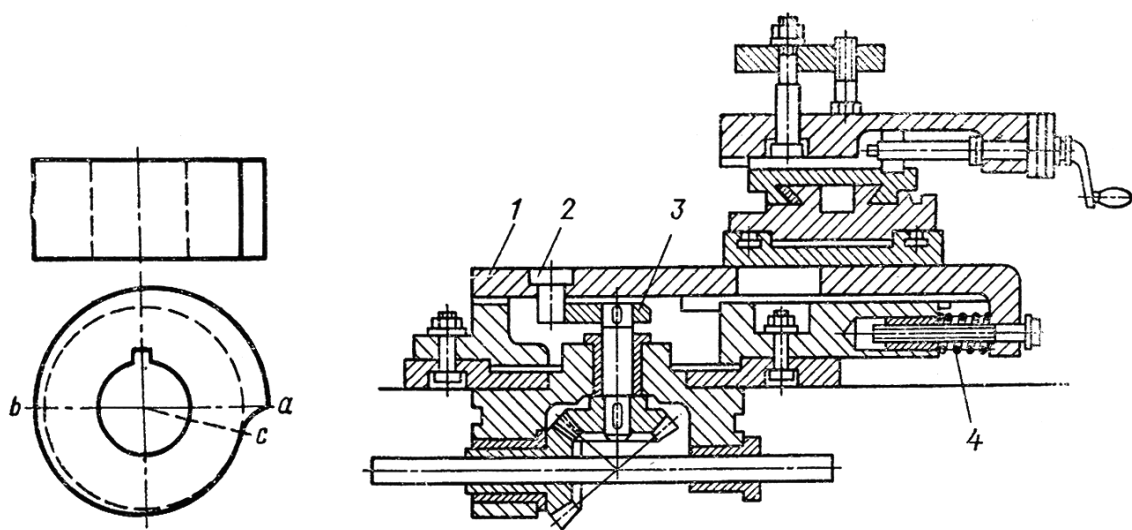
Эскизы сменного кулачка и суппорта токарно-затыловочного станка
